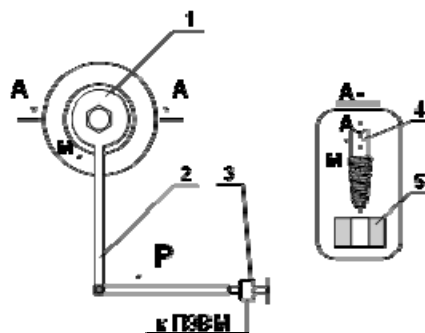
Схема испытаний процесса нарезания внутренней резьбы. 1 – приспособление, 2 – рычаг, 3 – датчик, 4 – инструмент, 5 – заготовка
